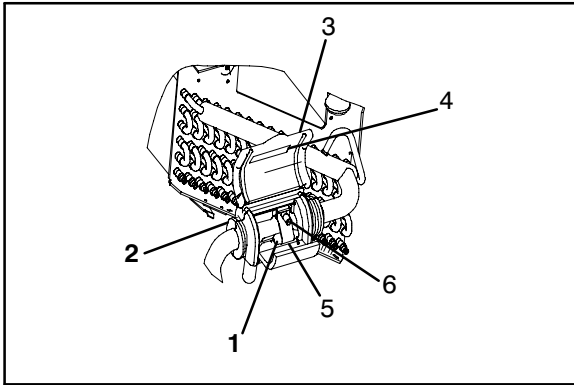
Procedimiento de soldadura fuerte de la válvula de expansión termostática hermética
